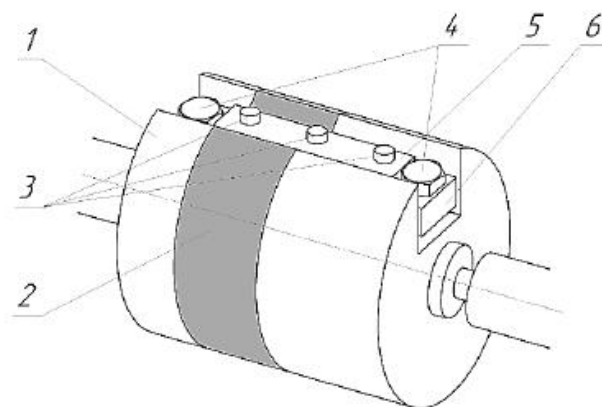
Приспособление для обработки листов и лент методом ДР на токарном станке
